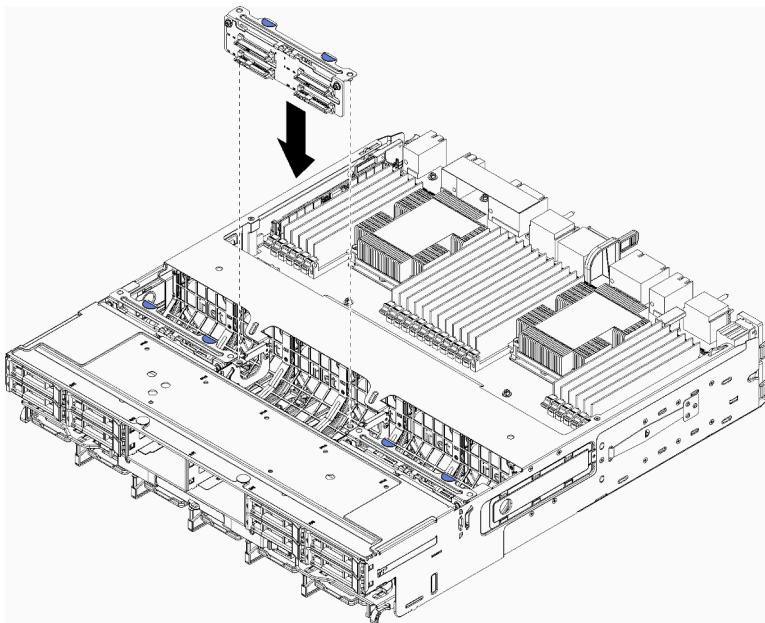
Installazione del backplane dell'unità disco fisso (superiore)
